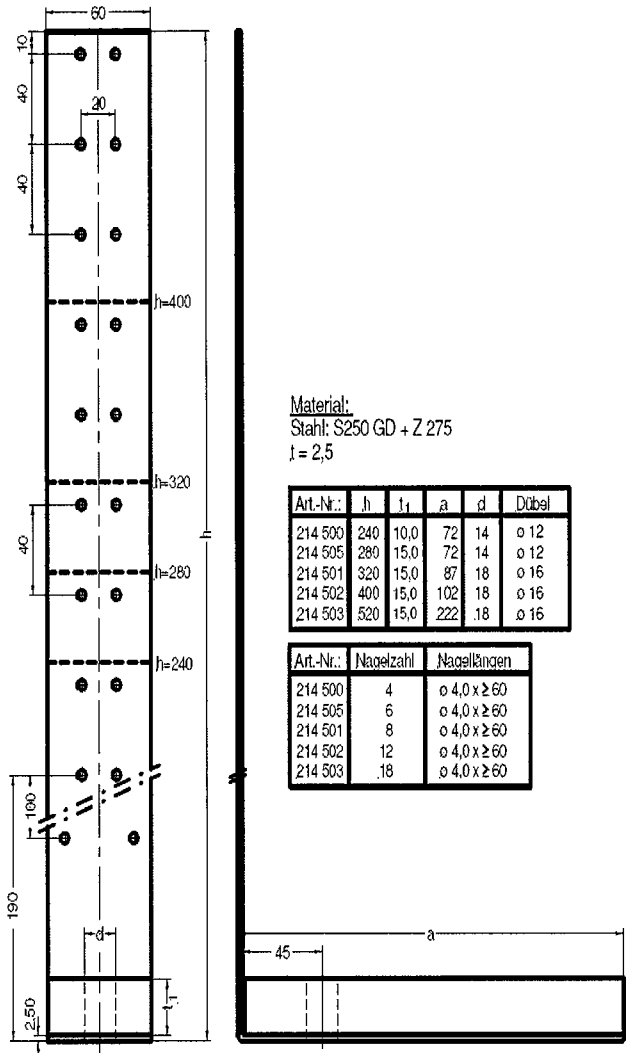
Maße des Zugankers Typ 1; Breite 60 mm
